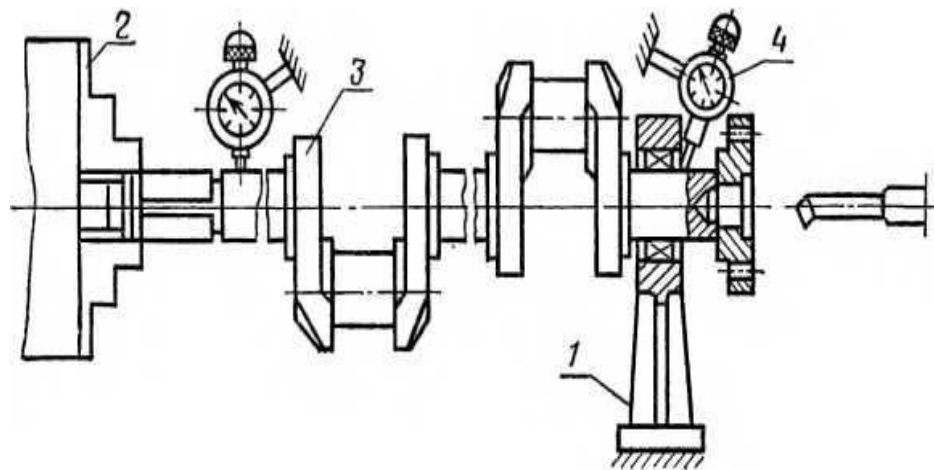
Схема встановлення колінчастого вала на токарному верстаті для обробки гнізда під підшипник: 1 - люнет; 2 - кулачковий патрон; 3 - колінчастий вал; 4 - індикатор.
